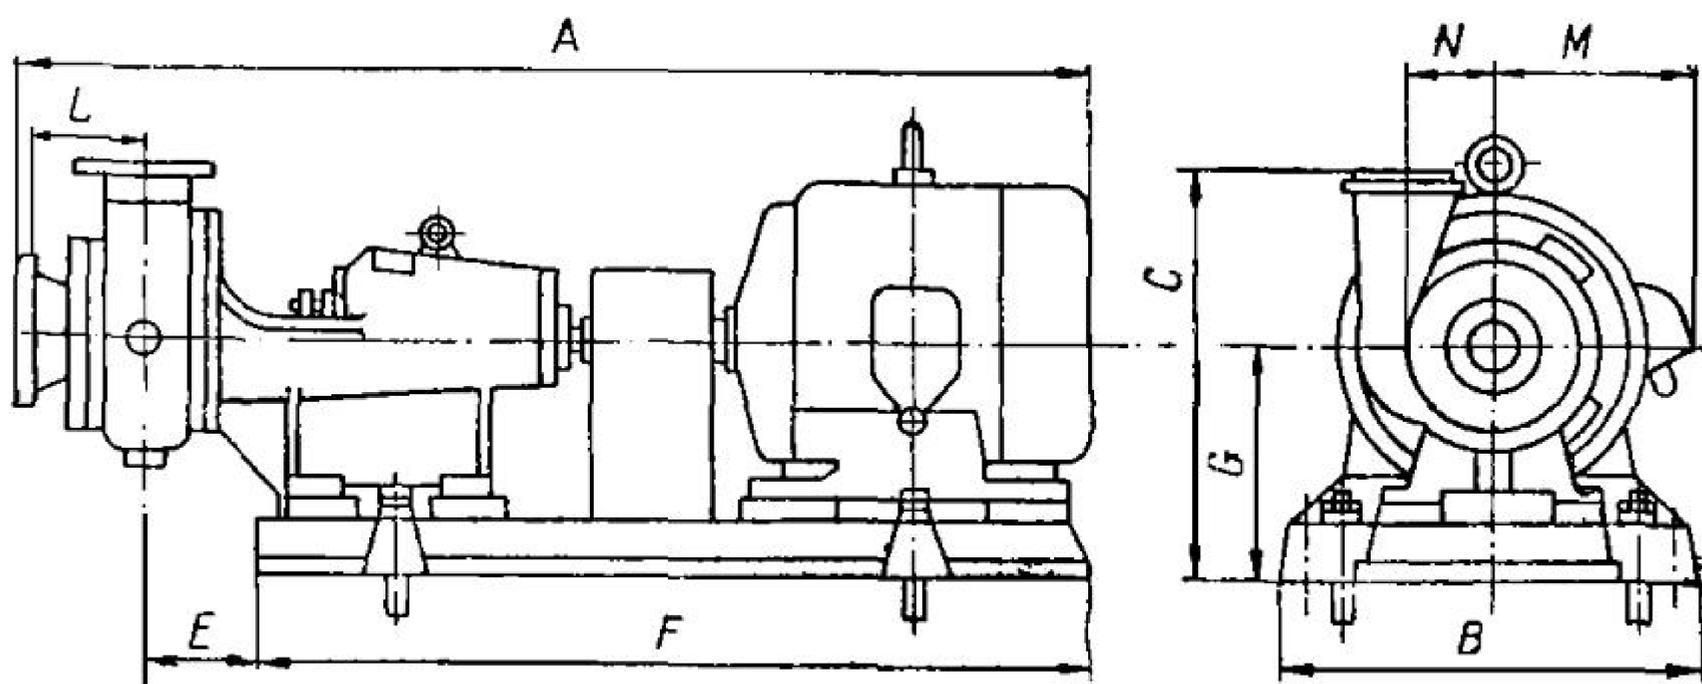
Общий вид и габаритные размеры насосов типа К (СД, Гр) с электродвигателями
